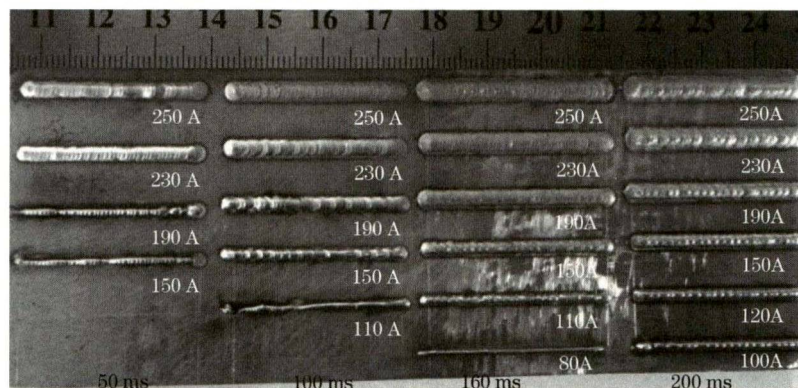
不同冷焊电流和时间下 TIG 冷焊熔敷焊道的表面形貌
